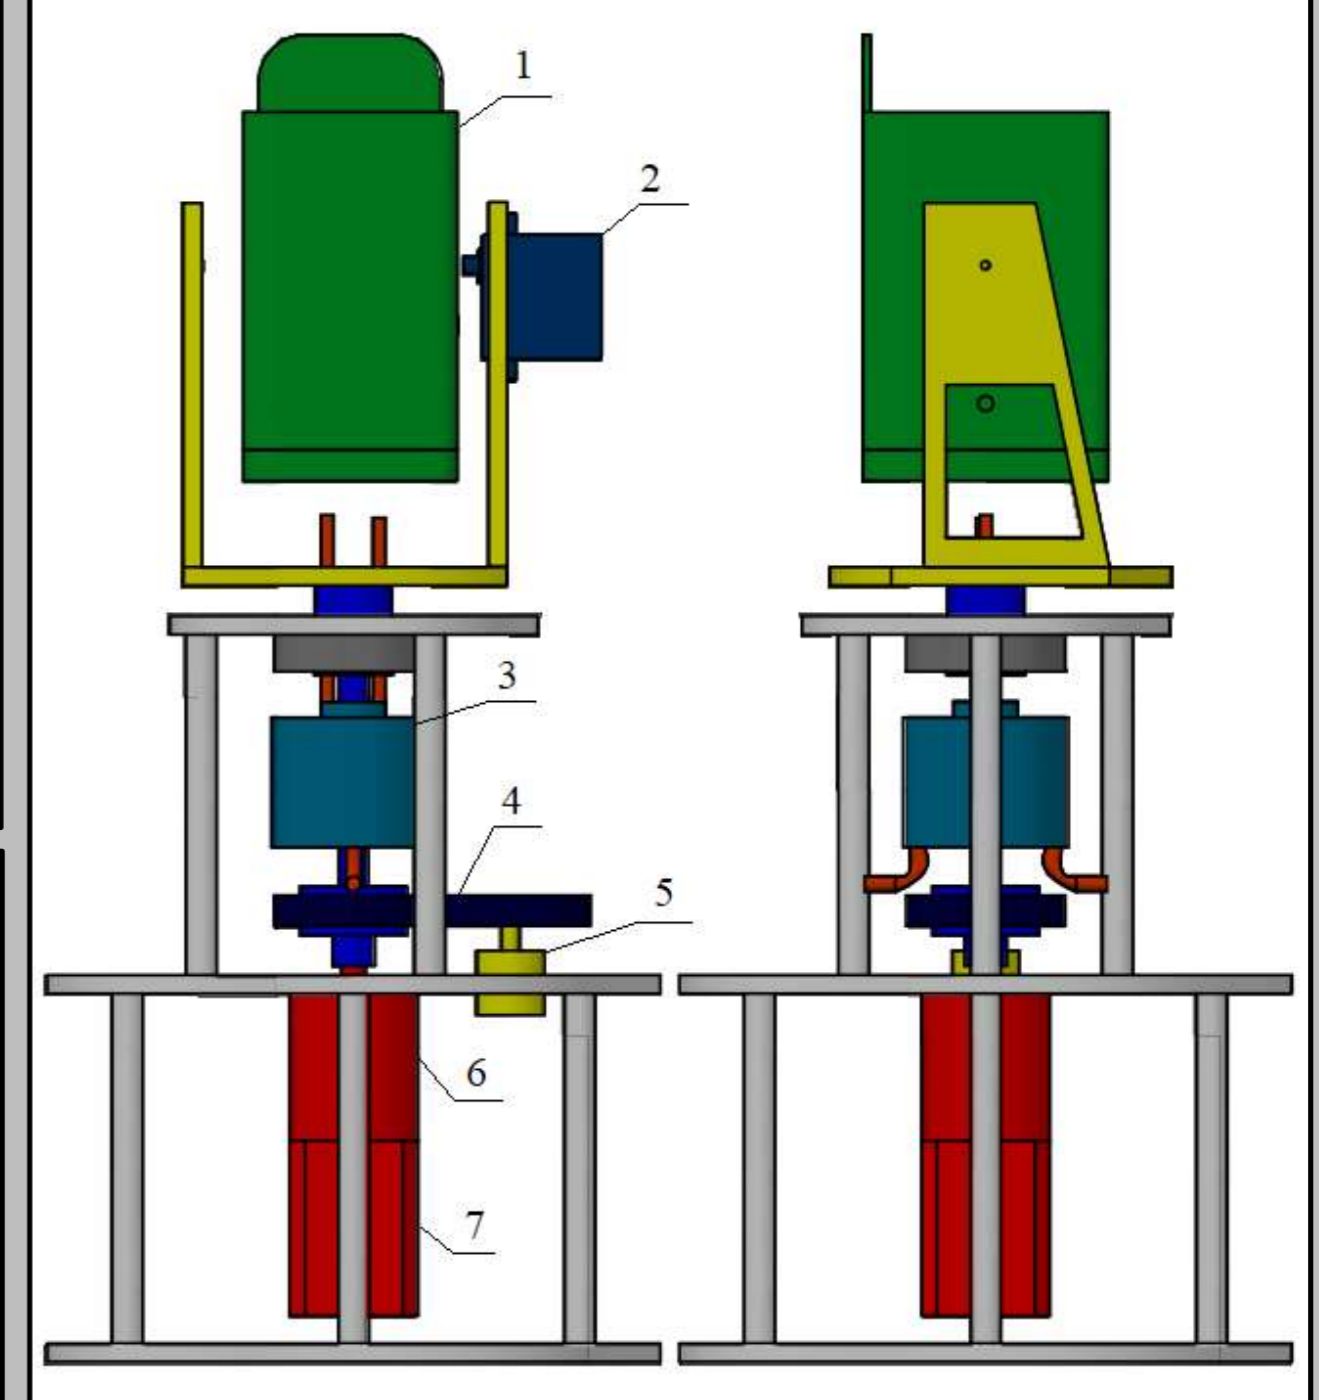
Конструкция нового обзора неба на базе IP-камеры, вид спереди, вид сбоку.
